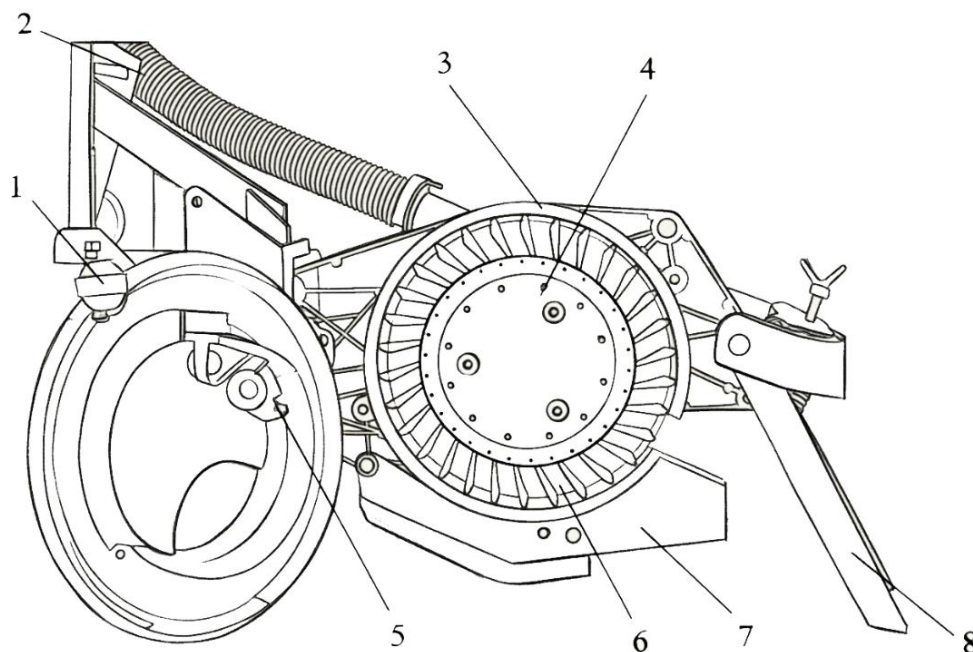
Конструктивная схема высевающего диска сеялки точного высева (1 – регулировочный рычаг съемника семян; 2 – воздуховод; 3 – корпус высевающего аппарата; 4 – высевающий диск; 5 – съемник семян; 6 – крыльчатый диск; 7 – сошник; 8 – загортач)
